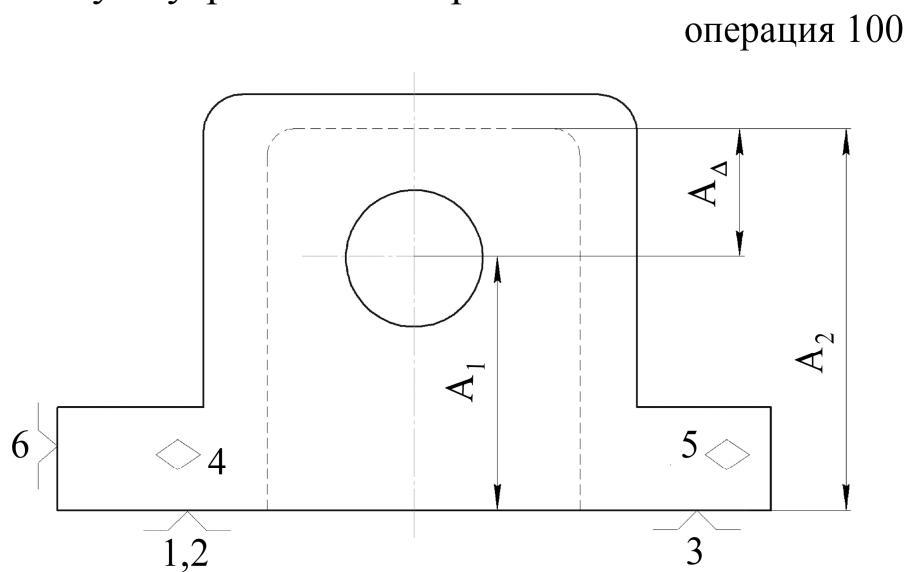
Получение расстояния от оси обрабатываемого отверстия до внутренней необрабатываемой поверхности корпуса
